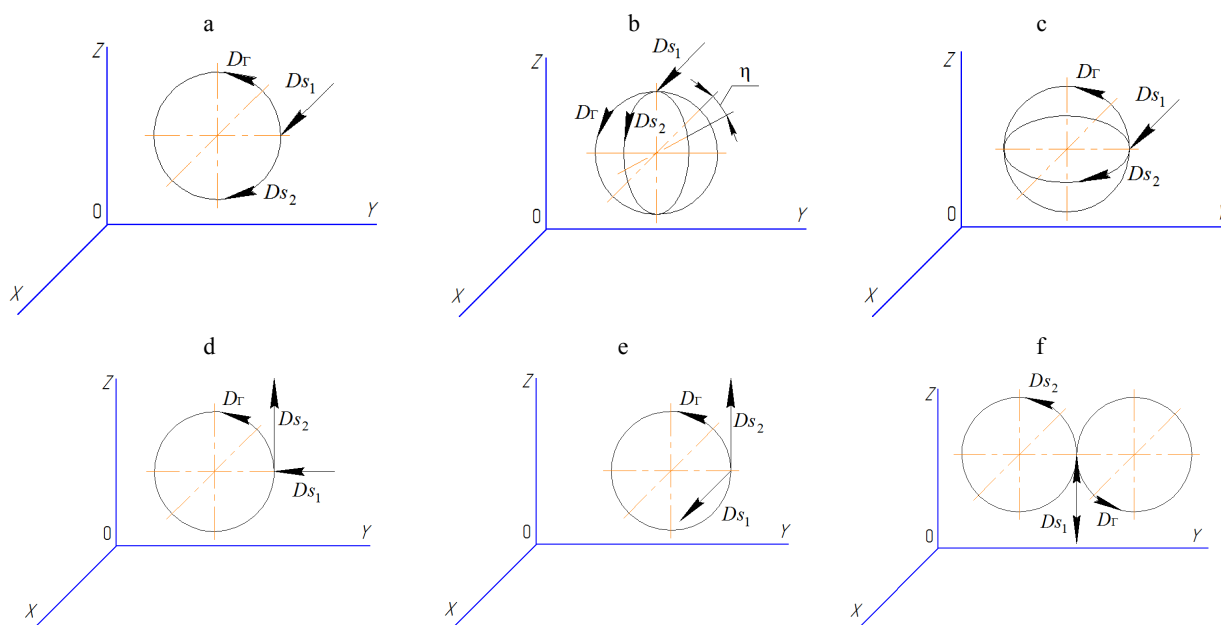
Кинематические схемы резания: а – обработка охватывающими фрезами (зенкерами) цилиндрической или конической поверхности; б, с – то же неполной сферической поверхности;
